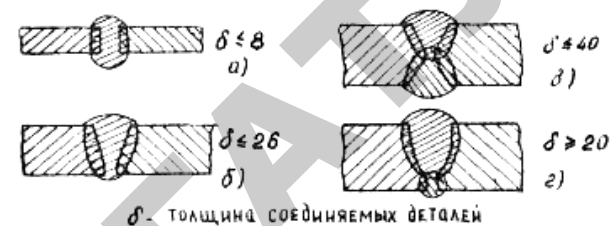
Виды стыковых сварных соединений
